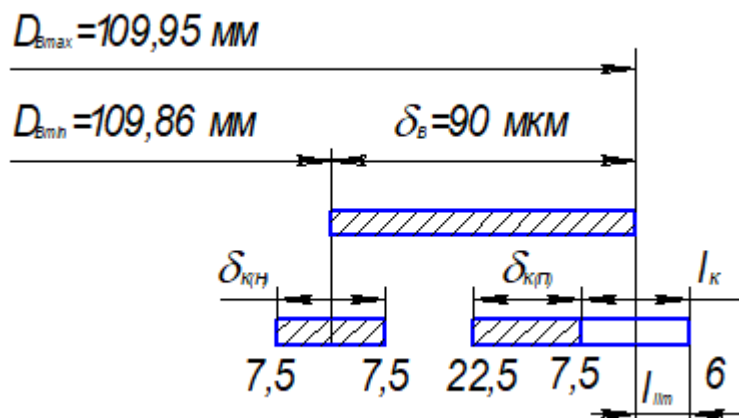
Положение полей допусков калибра относительно предельных размеров изделия.
